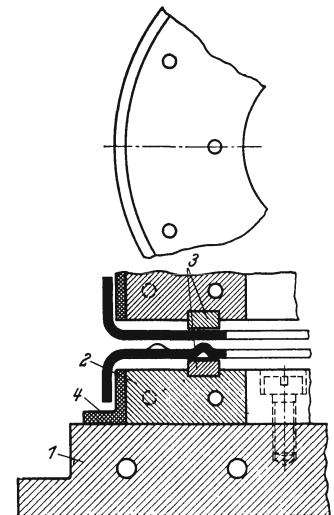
Buckelschweißwerkzeug mit Einsatz-elektroden für ein großes Werkstück.
